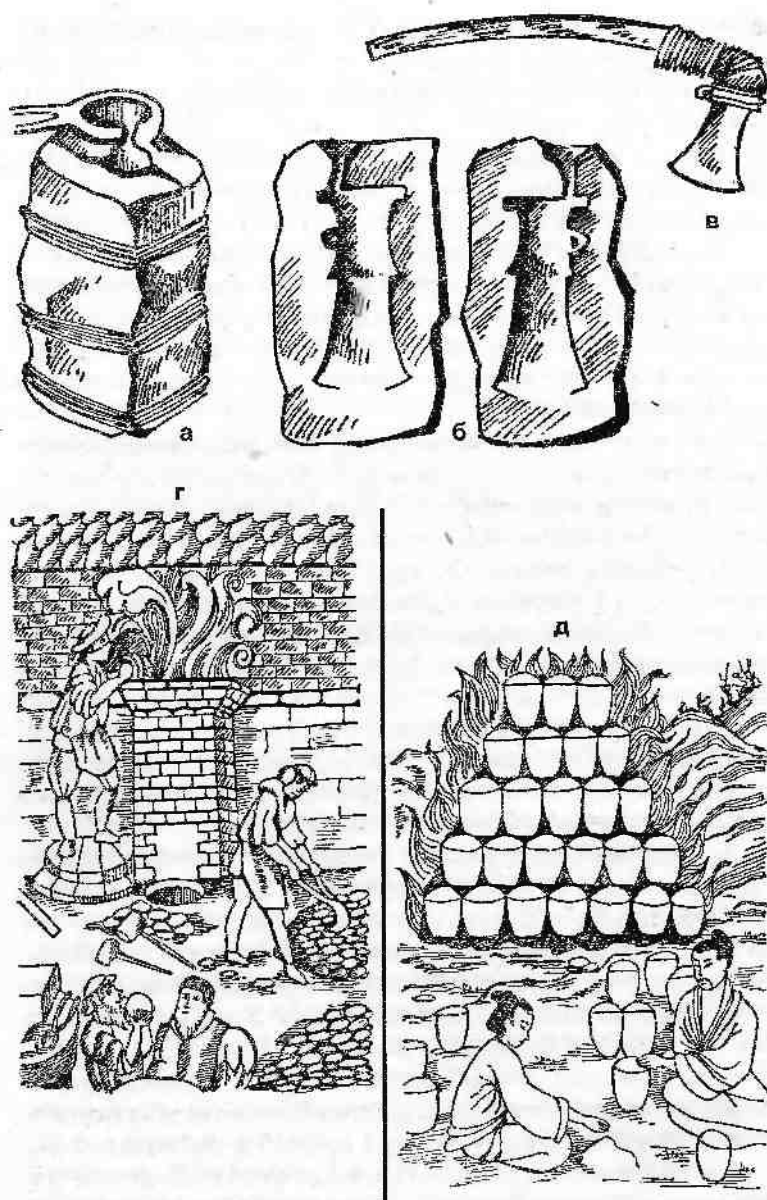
Начало металлургии: а, б, в — отливка медного топора (б — полуформы, в — готовый топор), г — кирпичное производство, д — тигельная плавка металла в Китае
